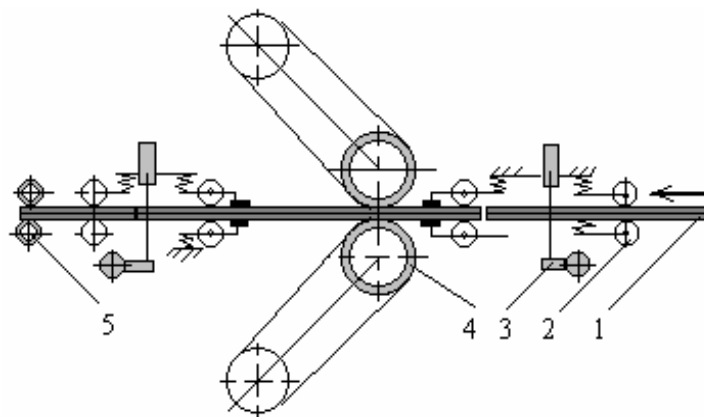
Схема станка ДКШ-1: 1 - шлифуемый материал; 2 - подающие вальцы; 3 - механизм подъема верхней станины; 4 - шлифовальный агрегат; 5 - щетки
